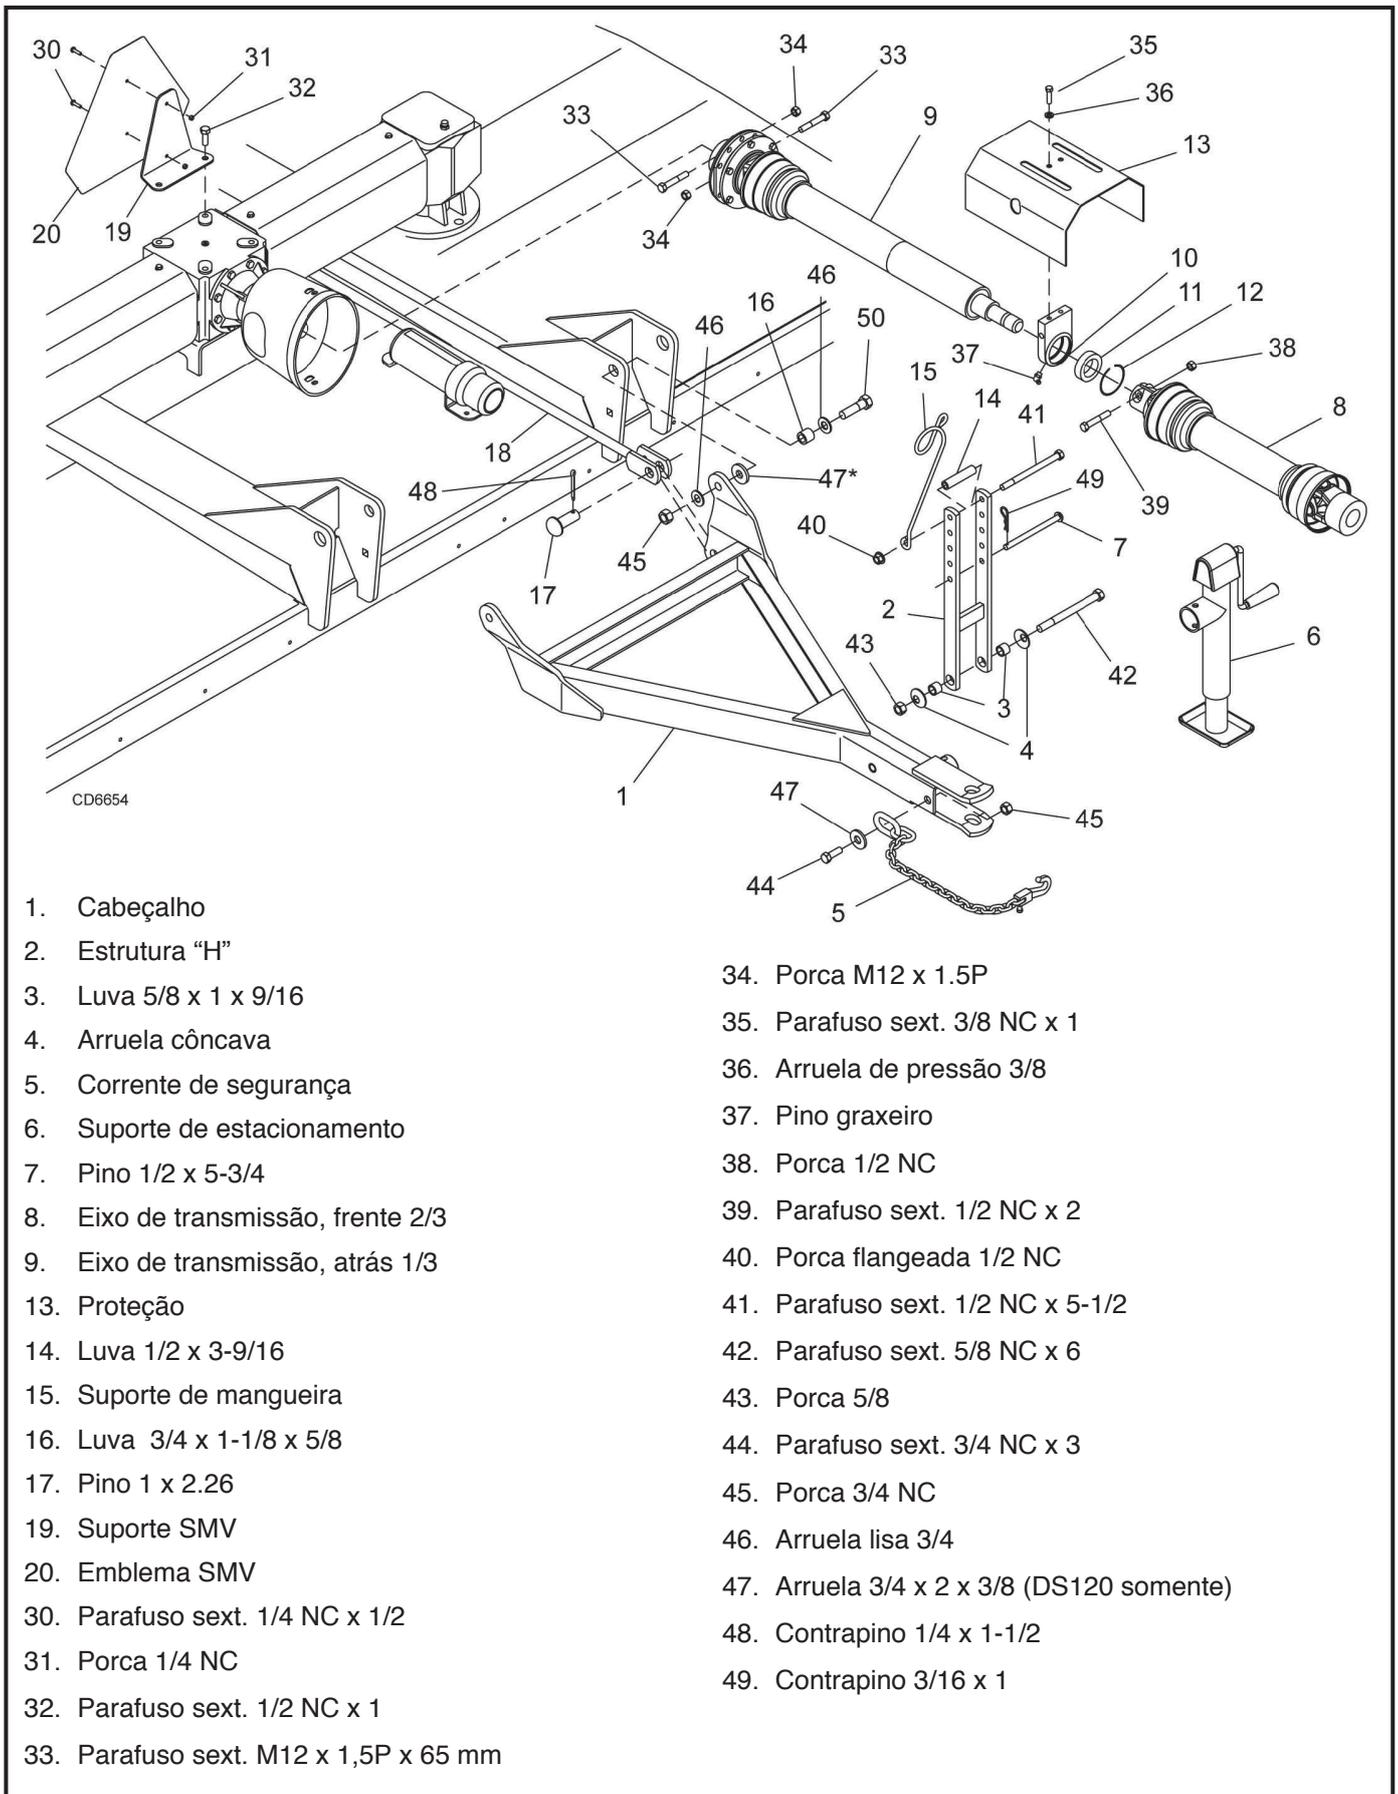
Instalação do Cabeçalho e Eixo de Transmissão DS96 e DS120
